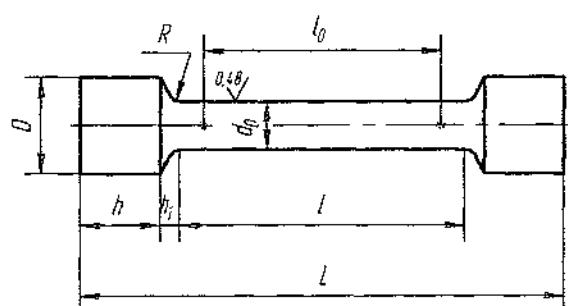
Образец для испытания металла шва на статическое растяжение
